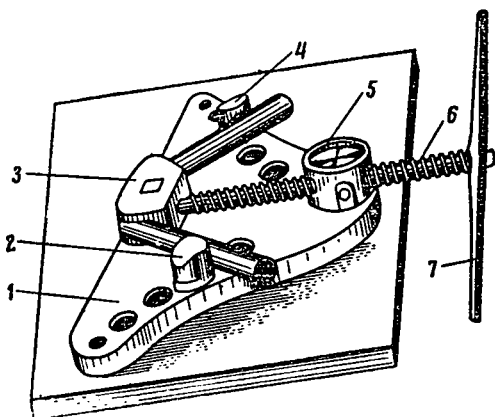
Ручное приспособление для гибки труб со сменной оправкой
